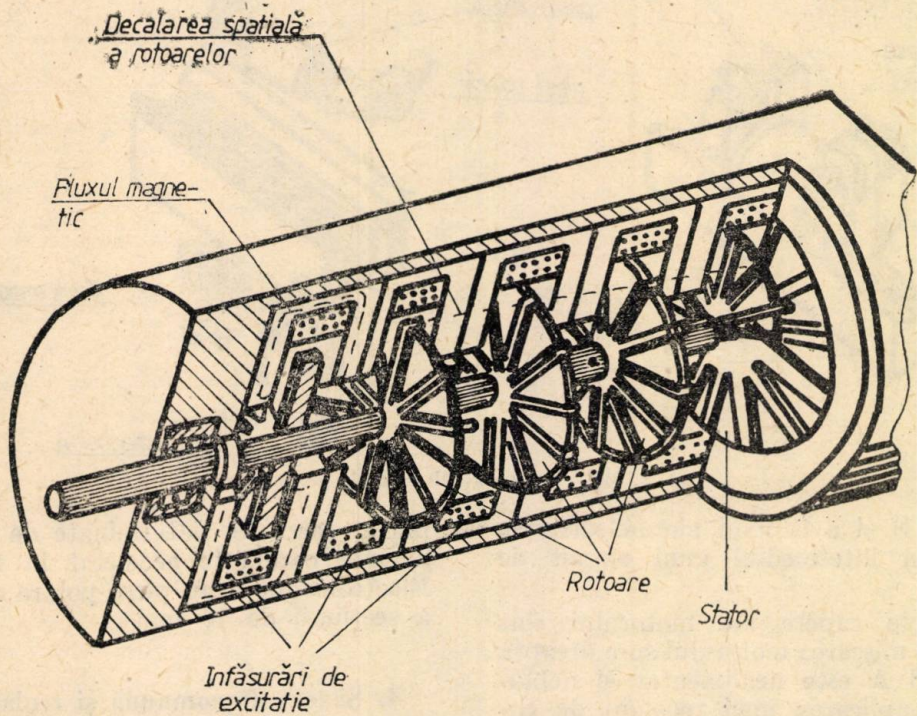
Motorul pas cu pas cu rotor multi-disc.
